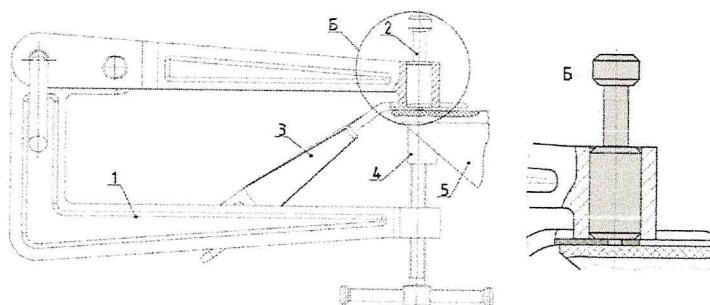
Разрез кондукторной скобы, выполненной по второму варианту
